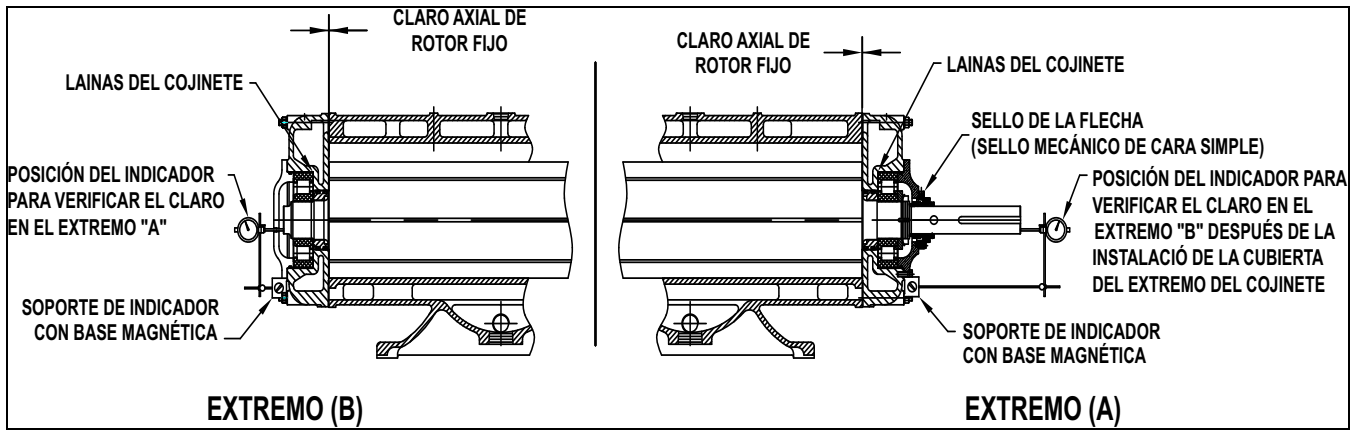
Claro axial del rotor (cojinetes posicionados por laines).
